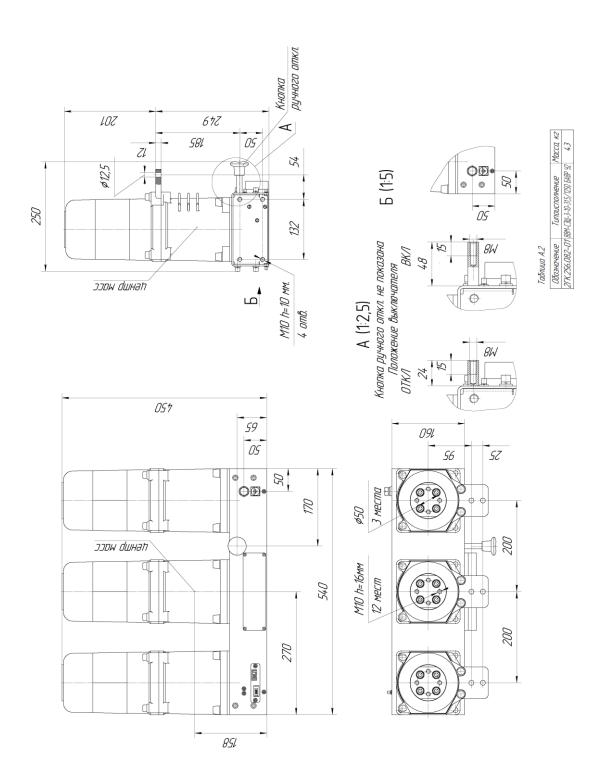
Габаритные, присоединительные и установочные размеры выключателя типа BBM-СЭЩ-3-10-31,5/1250 БАВР У2
